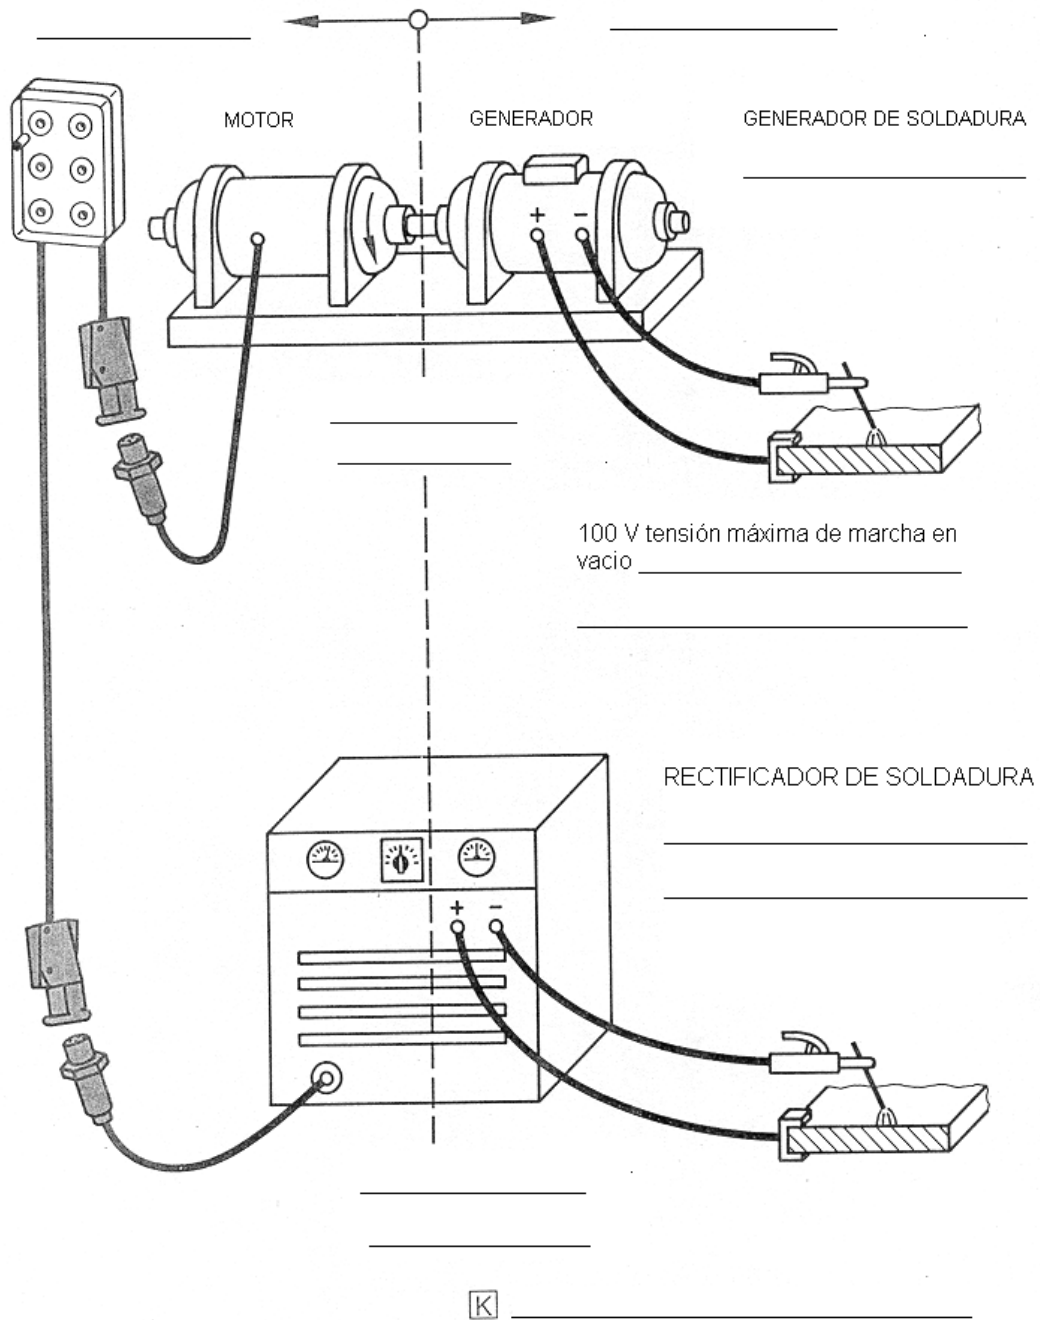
Conexión y mantenimiento del transformador de soldadura
